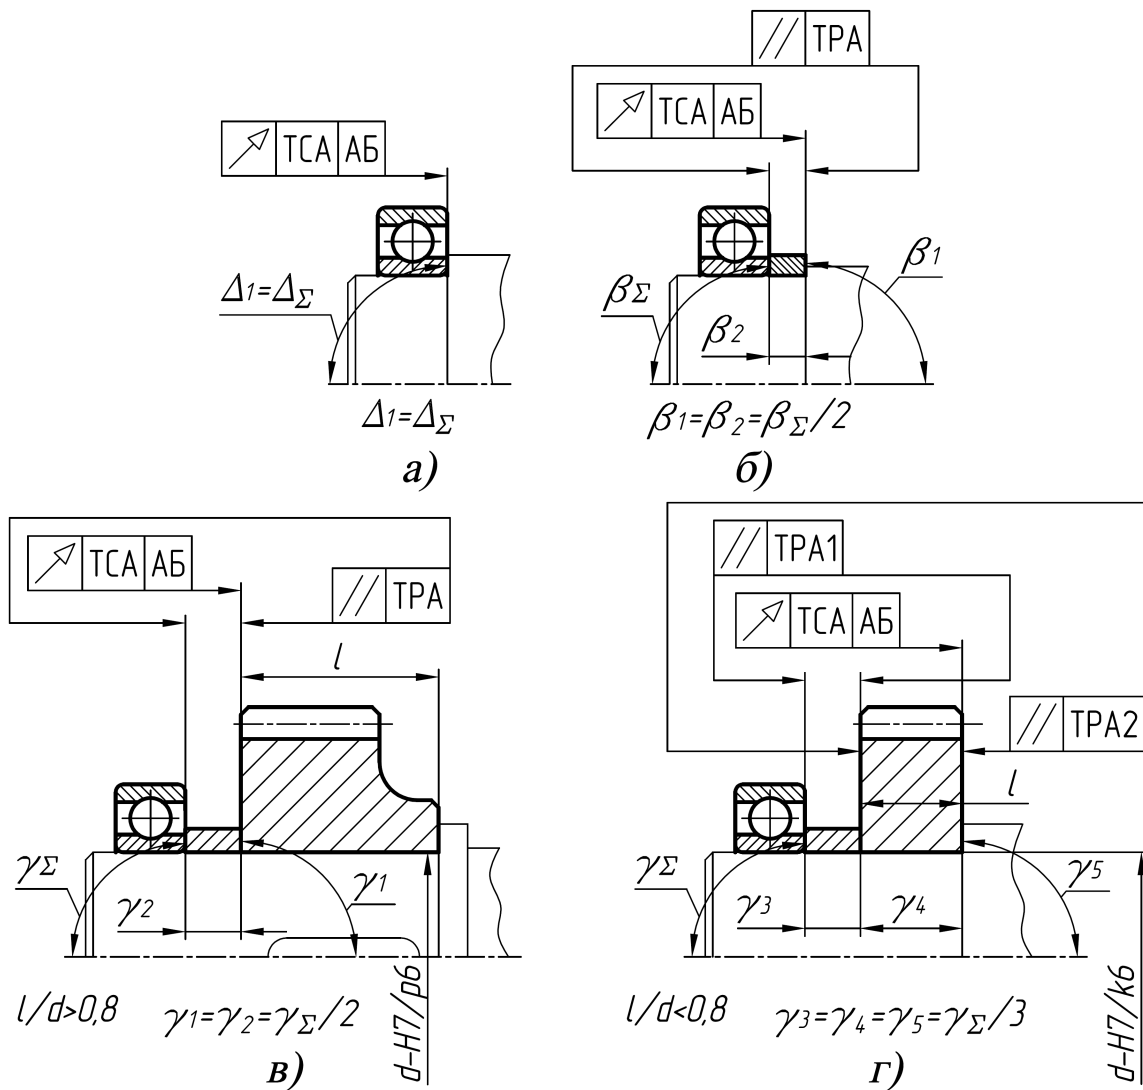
Схеми установки внутрішнього кільця підшипника кочення;
